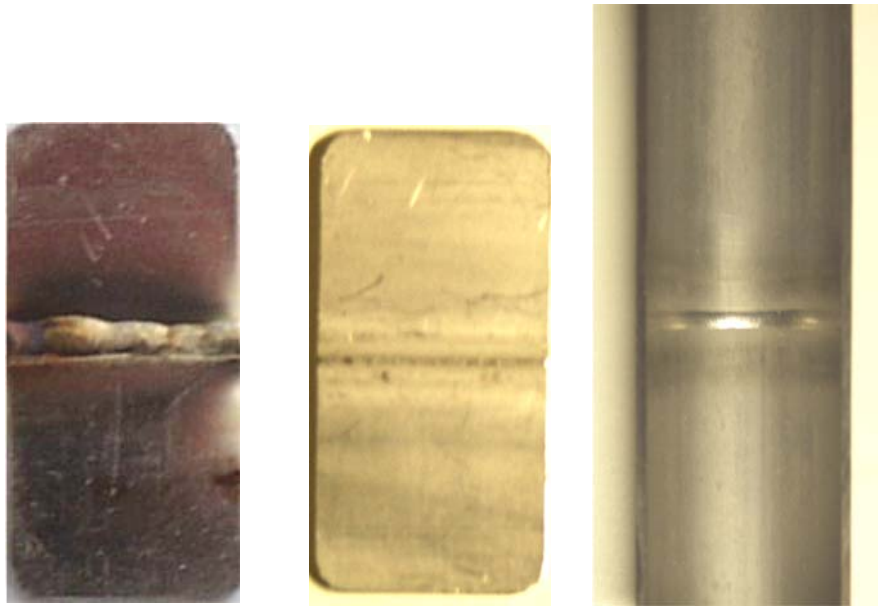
Aufnahmen der verwendeten Schweißnähte (links: WIG-Naht auf Probe-Plättchen, Mitte: Laser-Naht auf Probe-Plättchen, rechts: Innenseite der Orbitalnaht)
